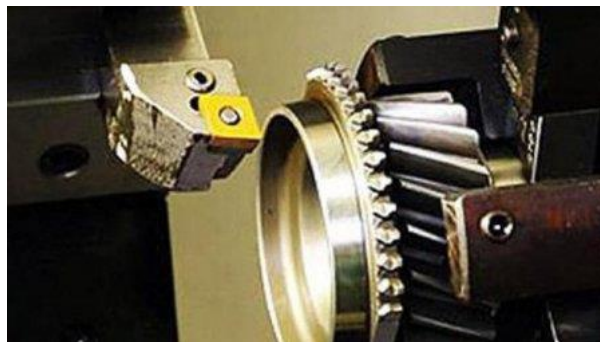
Приклад різця та деталі, що оброблюється на токарному верстаті
